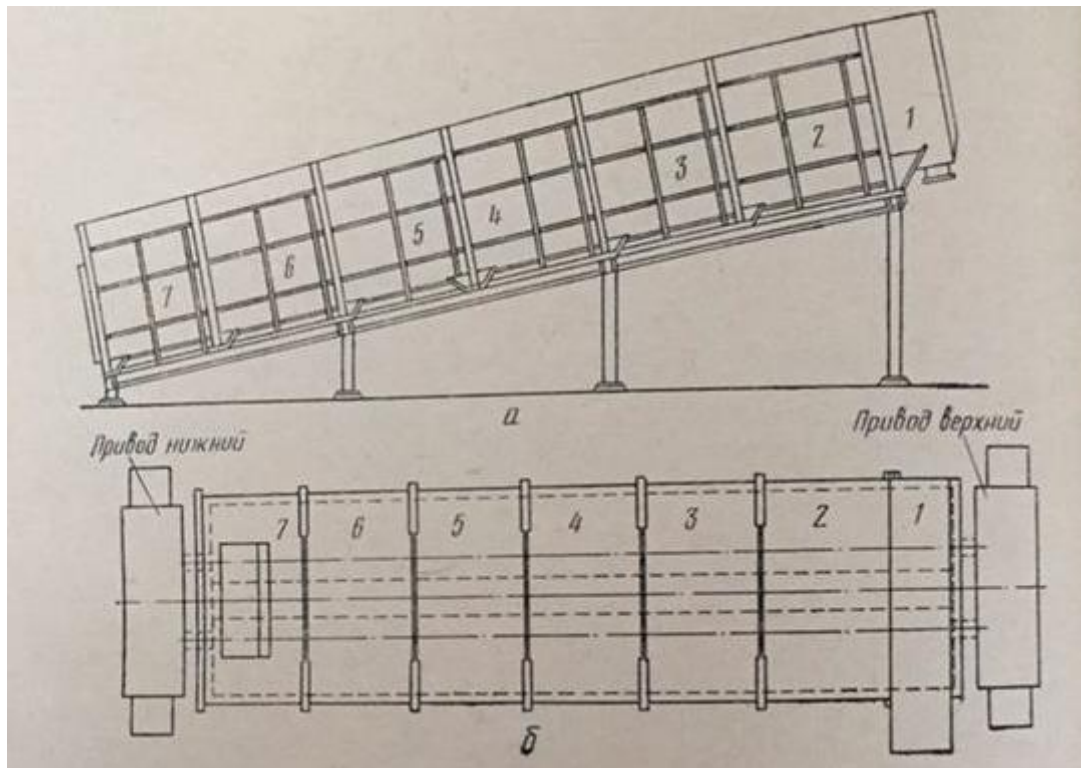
Схема збірки секцій корпусу дифузійного апарату:
